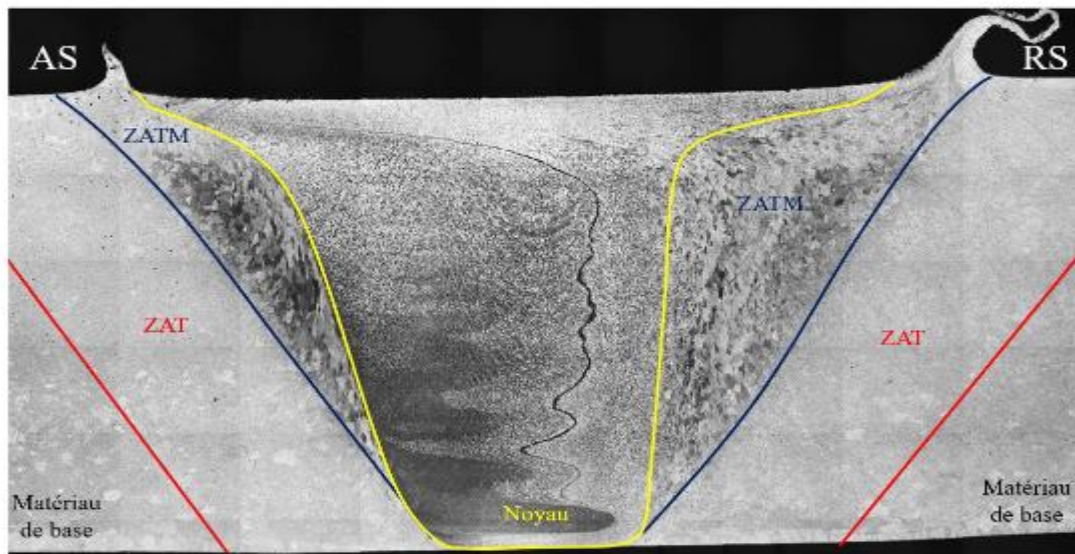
Macrostructure d'une soudure d'alliage 6061-T6 de 9,53 mm [12]
